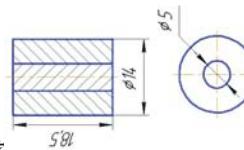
Заготовка под выдавливание компрессорной лопатки
